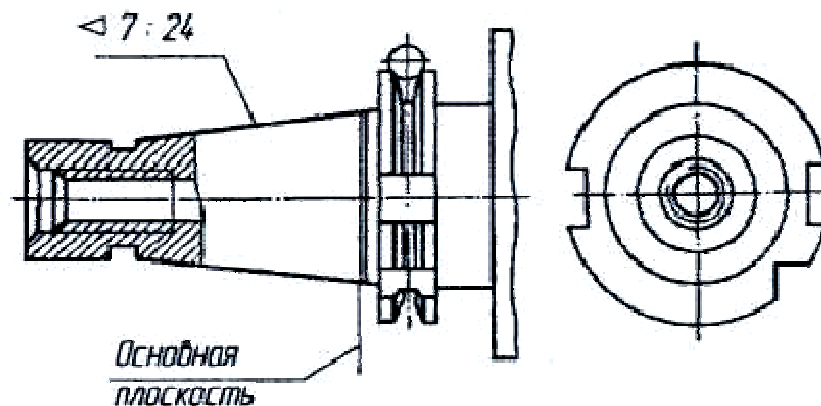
Хвостовик шпиндельных оправок станков сверлильно-фрезерно-расточной группы
